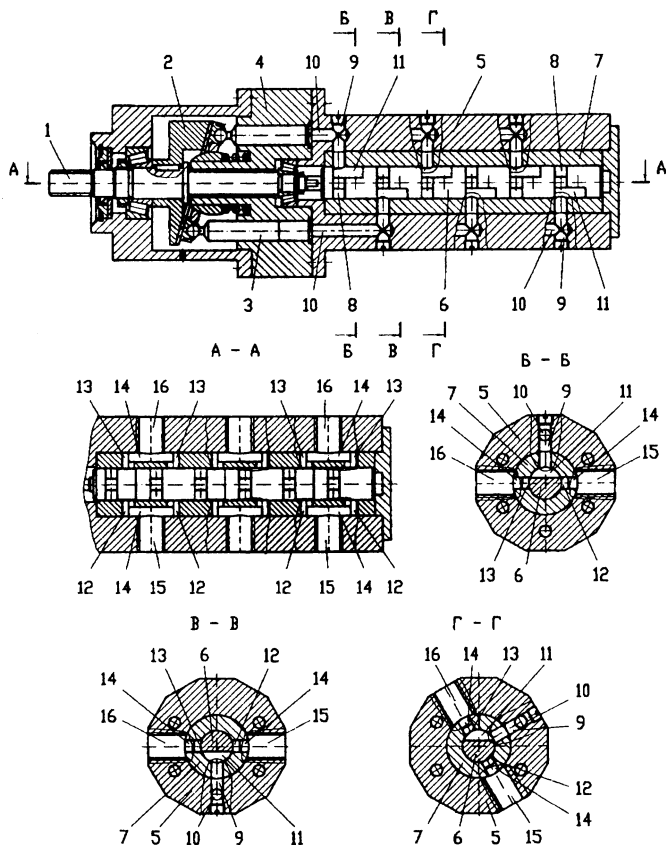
Аксиально-поршневая гидромашина с неподвижным блоком цилиндров: 1 – ведущий вал; 2 – наклонная шайба; 3 – поршень; 4 – блок цилиндров; 5 – корпус гидрораспределителя; 6 – вал гидрораспределителя; 7 – подшипник скольжения; 8 – кольцевая канавка; 9, 10, 15, 16 – каналы корпуса гидрораспределителя; 11 – сегментный паз; 12, 13 – каналы подшипника скольжения; 14 – пазы подшипника скольжения
